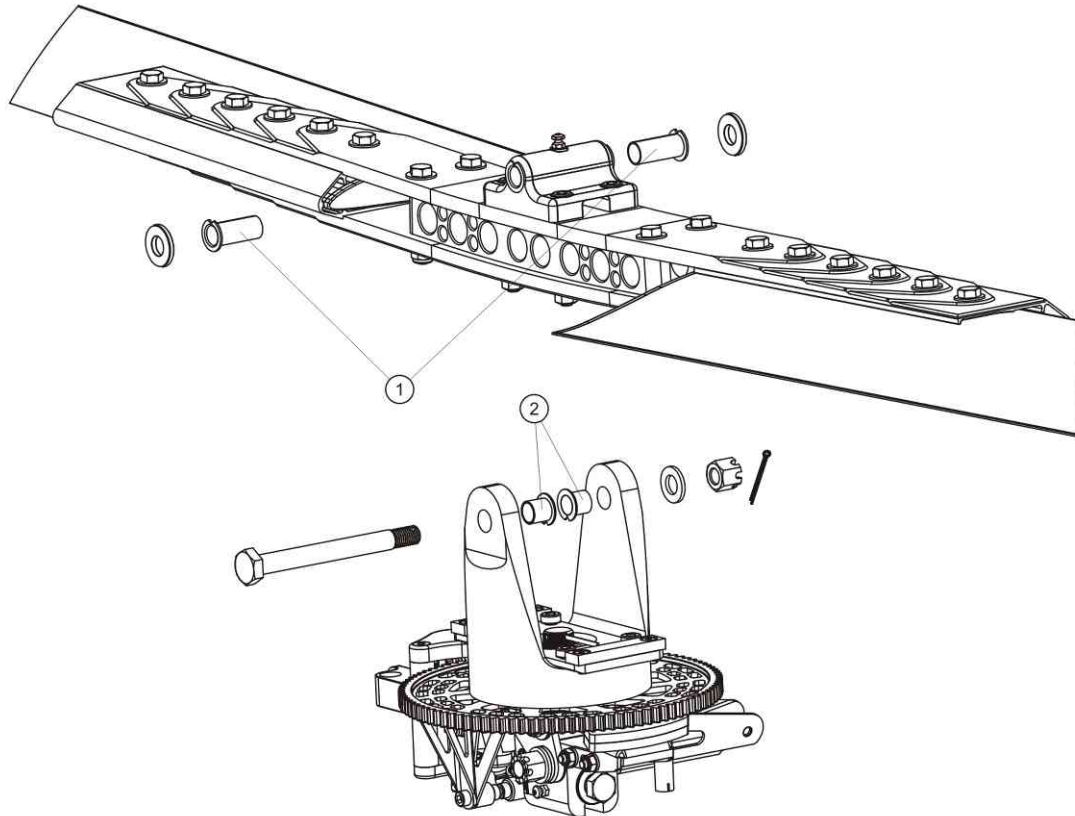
Teeterlager Buchsen, Block und Turm - Explosionsansicht
